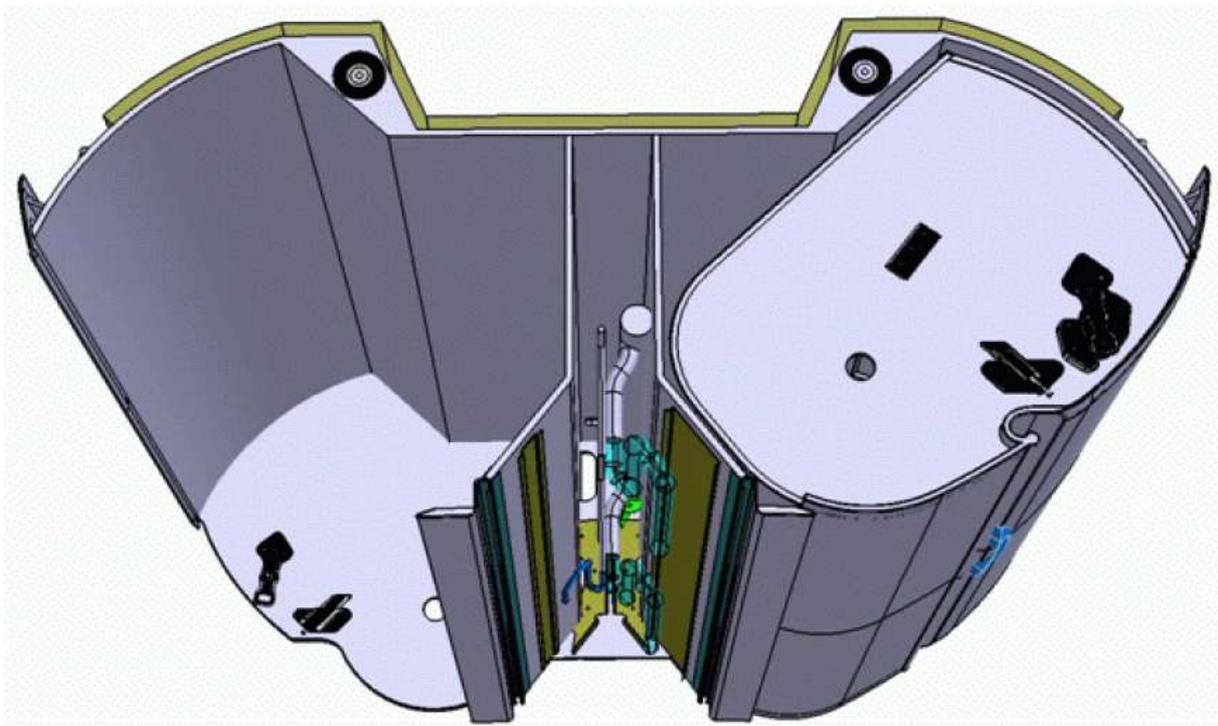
Box und Gehäuse einer zentralen, beweglichen Gepäckablage (Stefanik 2006)
